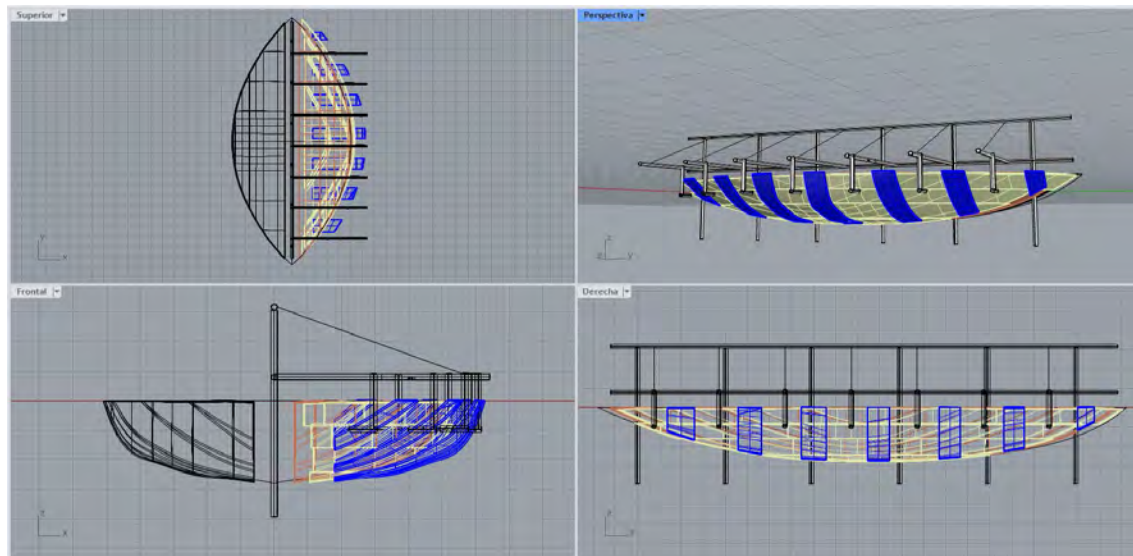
Boceto ilustrativo de la colocación de las exocuernas artificiales, para convertir el conjunto de soportes longitudinales en un elemento unitario y solidario entre sí longitudinal y transversalmente
